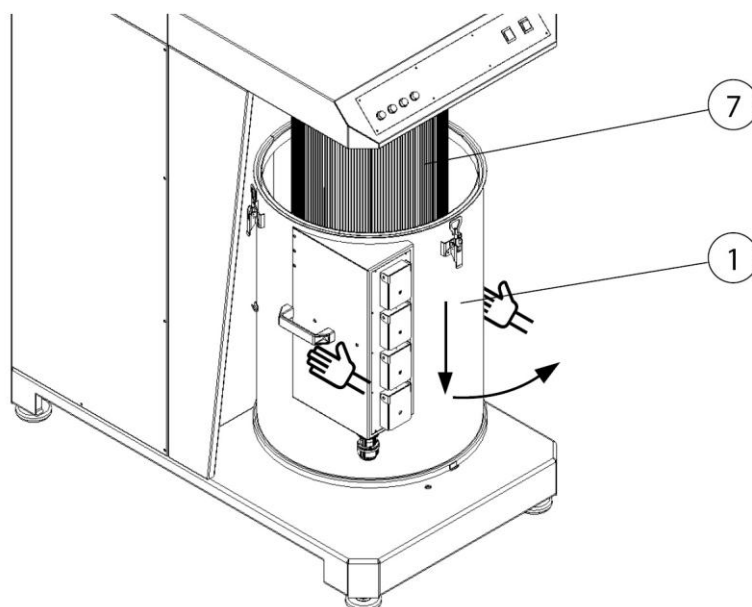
remplacement du filtre – démontage du boîtier de filtre
